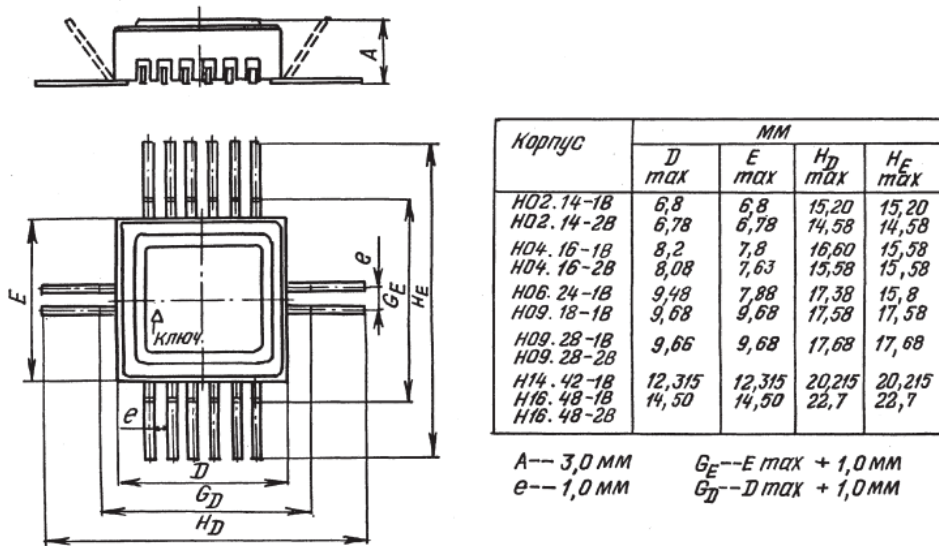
Габаритный чертеж корпуса H09.18-1B
